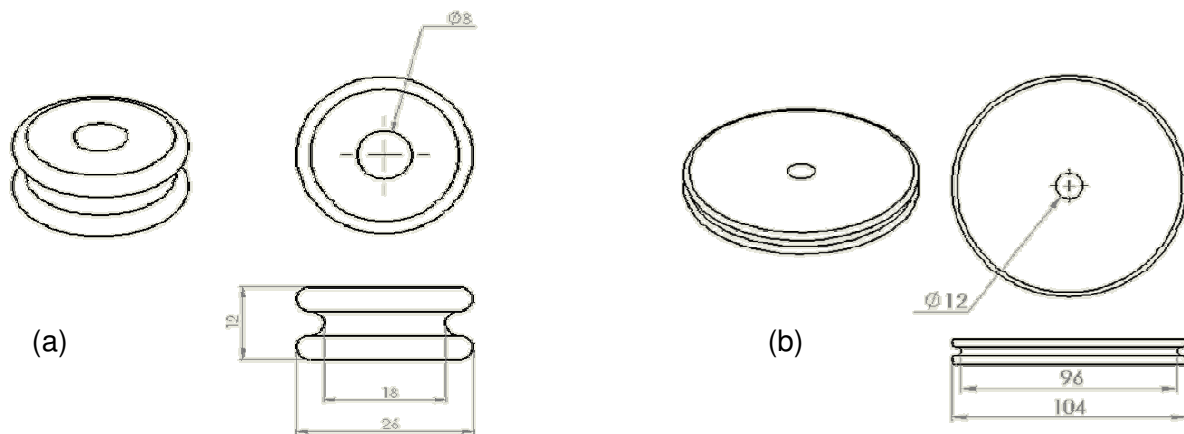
Dimension des poulies installées cotés moteur (a) et électrode (b) en millimètre.
